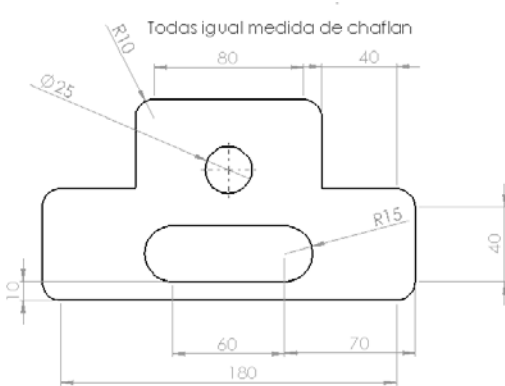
figura construida en MMC y con un valor de extrusión de 15 mm, la pieza se realiza en plano planta.
